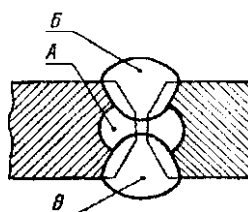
Сечение многопроходного сварного шва
